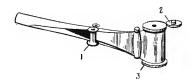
Саморазворачивающаяся аитенна: 1 — ведущий ролик; 2 — привод; 3 — барабан с лентой
